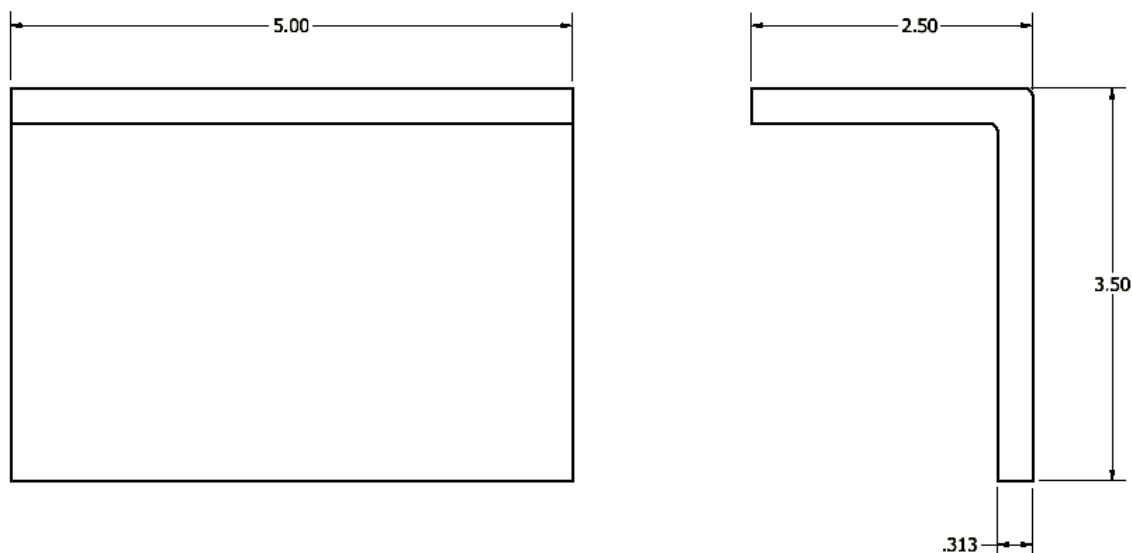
DIMENSIONES DEL ÁNGULO PARA LA CONEXIÓN SOLDADA DE DOBLE ÁNGULO
